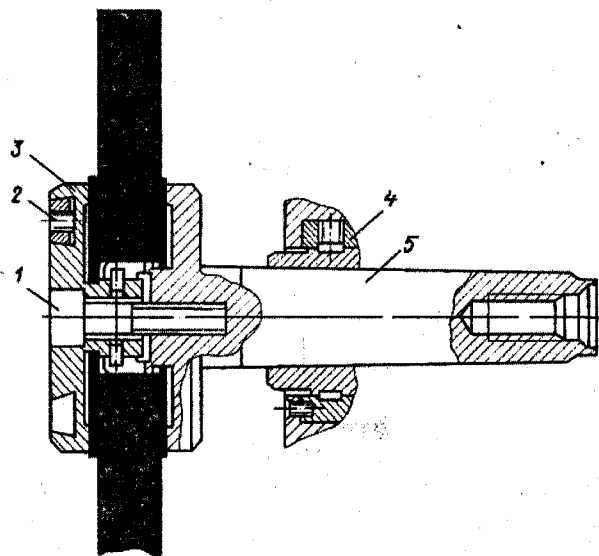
Оправка для крепления шлифовального круга на универсально-заточном станке
